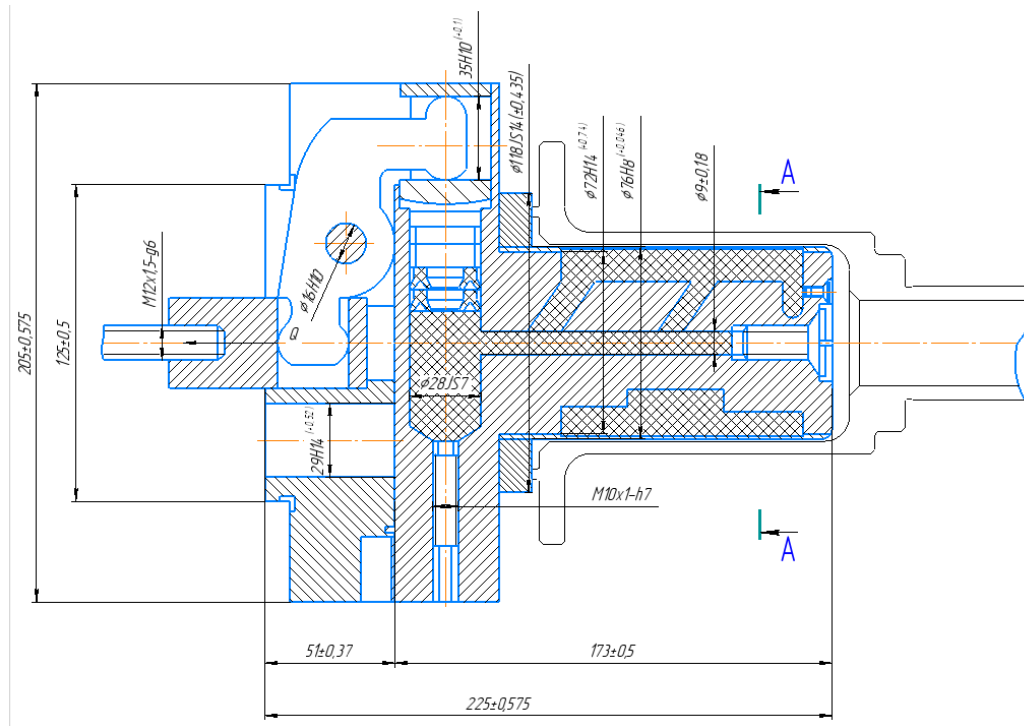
Консальная гидропластовая оправка и крепление детали.
